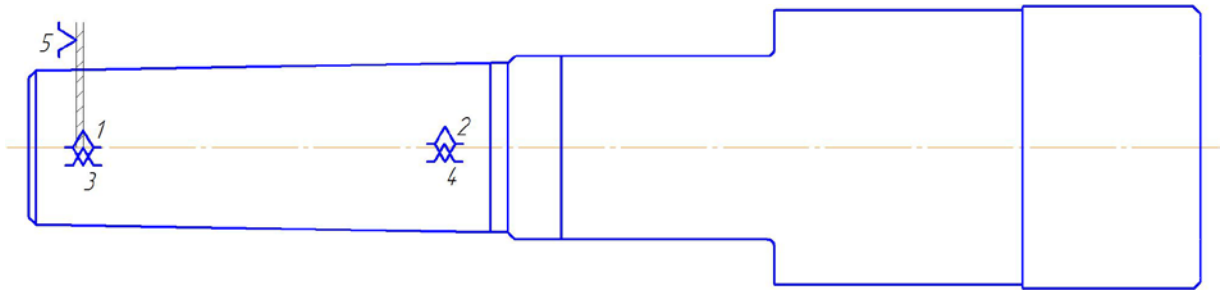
Теоретична схема базування деталі «Корпус борштанги» по загальній технологічній базі
